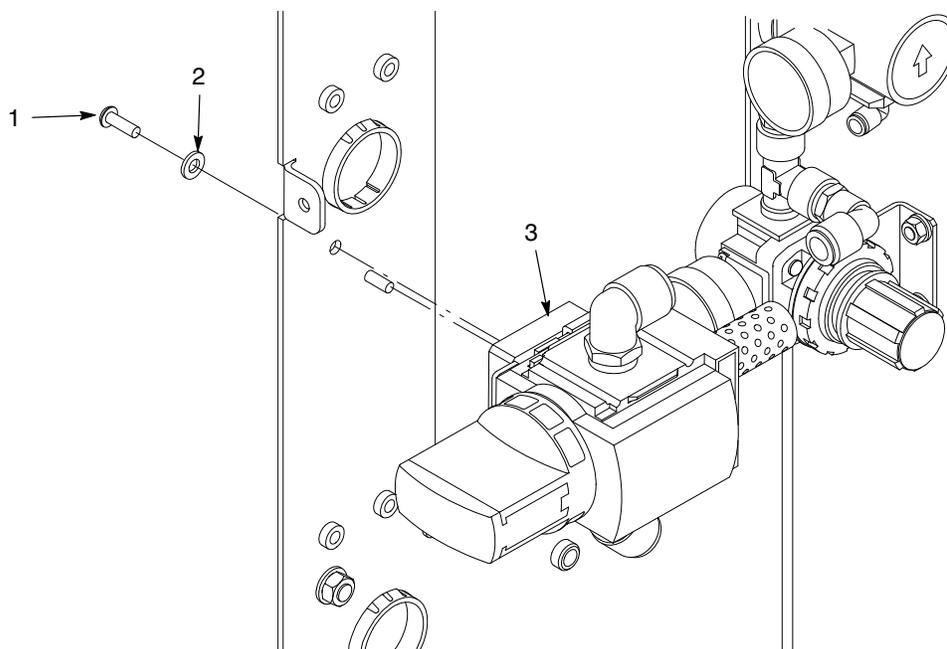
Dépose/remplacement de la vanne d'arrêt du moteur pneumatique
